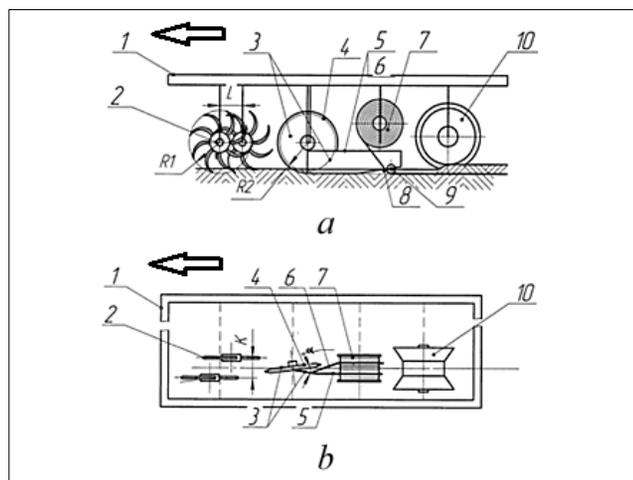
Агрегат для высева семенного материала в ленте: а – вид слева; б – вид сверху (<https://www1.fips.ru>)
